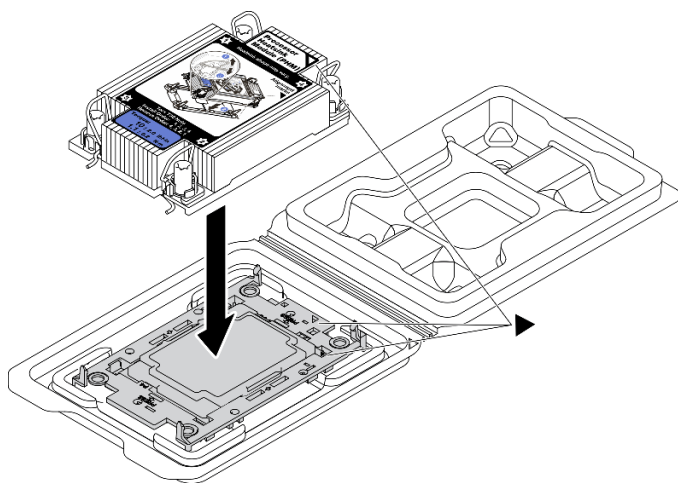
Assemblage du module de processeur-dissipateur thermique avec le processeur dans le plateau d'expédition
